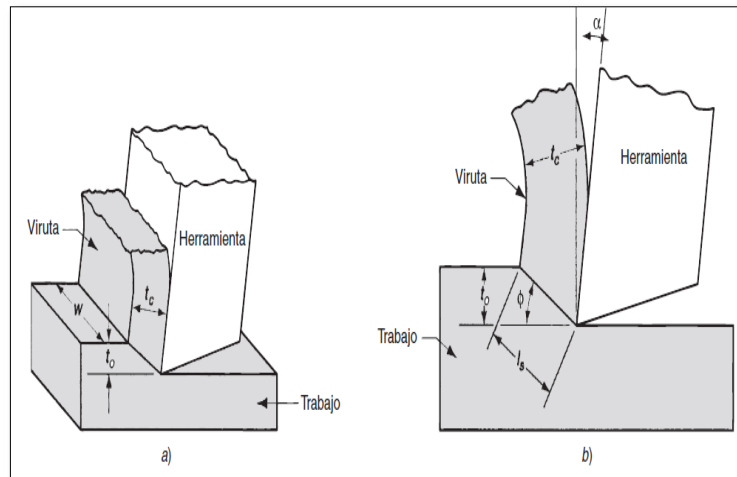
a) maquinado vista tridimensional y b) maquinado en un plano.
